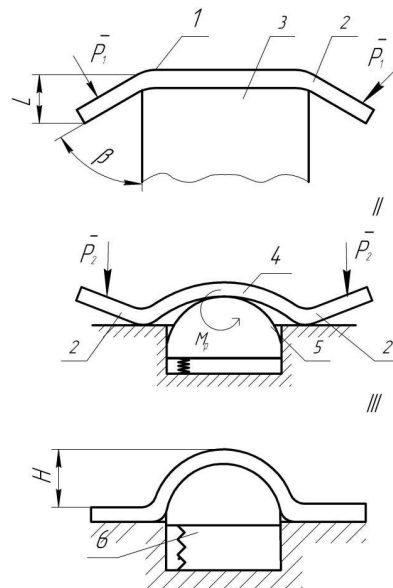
Схема самопроизвольного формоизменения рифта: P_1 , P_2 – деформирующие усилия; M_I – реактивный момент; 1 – 4. Заготовка и ее элементы; 5 – 6. Подпружиненный пуансон; I – III. Последовательность операций
